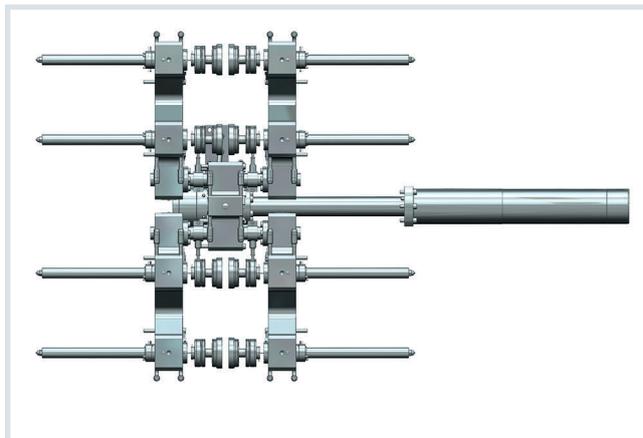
Die kompakte Auslegung mit Back-to-Back Anordnung der Antriebe trug zur Gewichtsreduzierung des Werkzeugs bei © Ewikon
